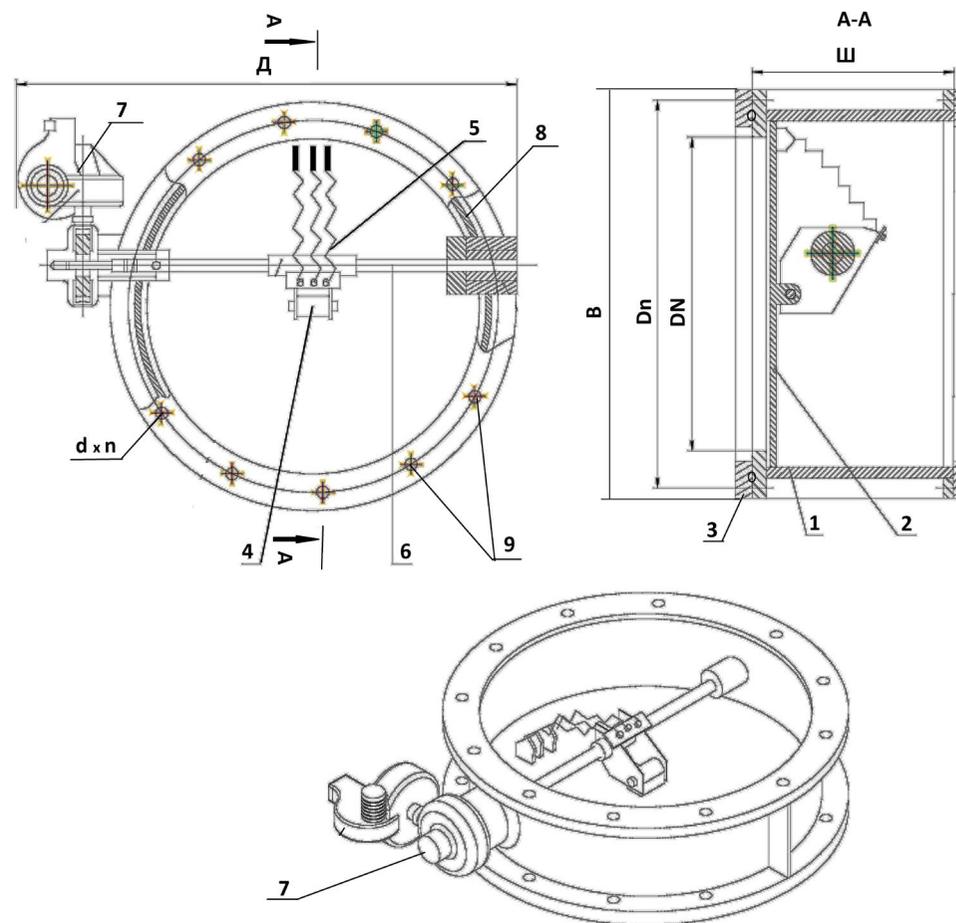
Герметический клапан вентиляционный ГК ИА
